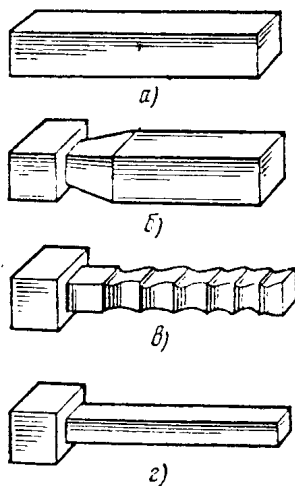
Схема вытяжки на квадратное сечение: а — нагретая заготовка, б — уступы, выполненные перебивкой, в — протянутая подбойкой последовательно с четырех сторон заготовка, г — окончательно отделанная плоской гладилкой заготовка
